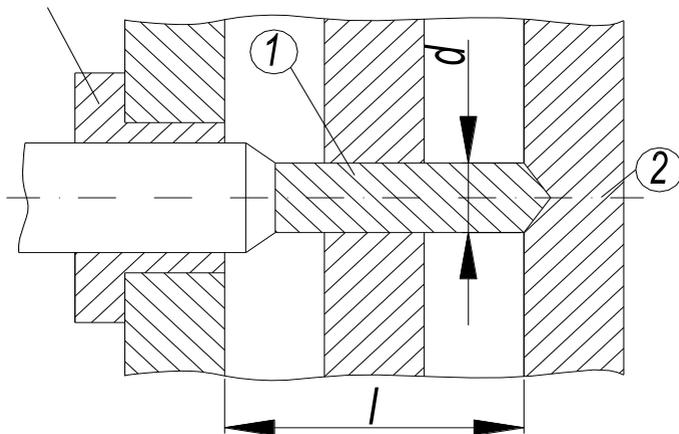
Пример обработки соосного отверстия – односторонняя схема
